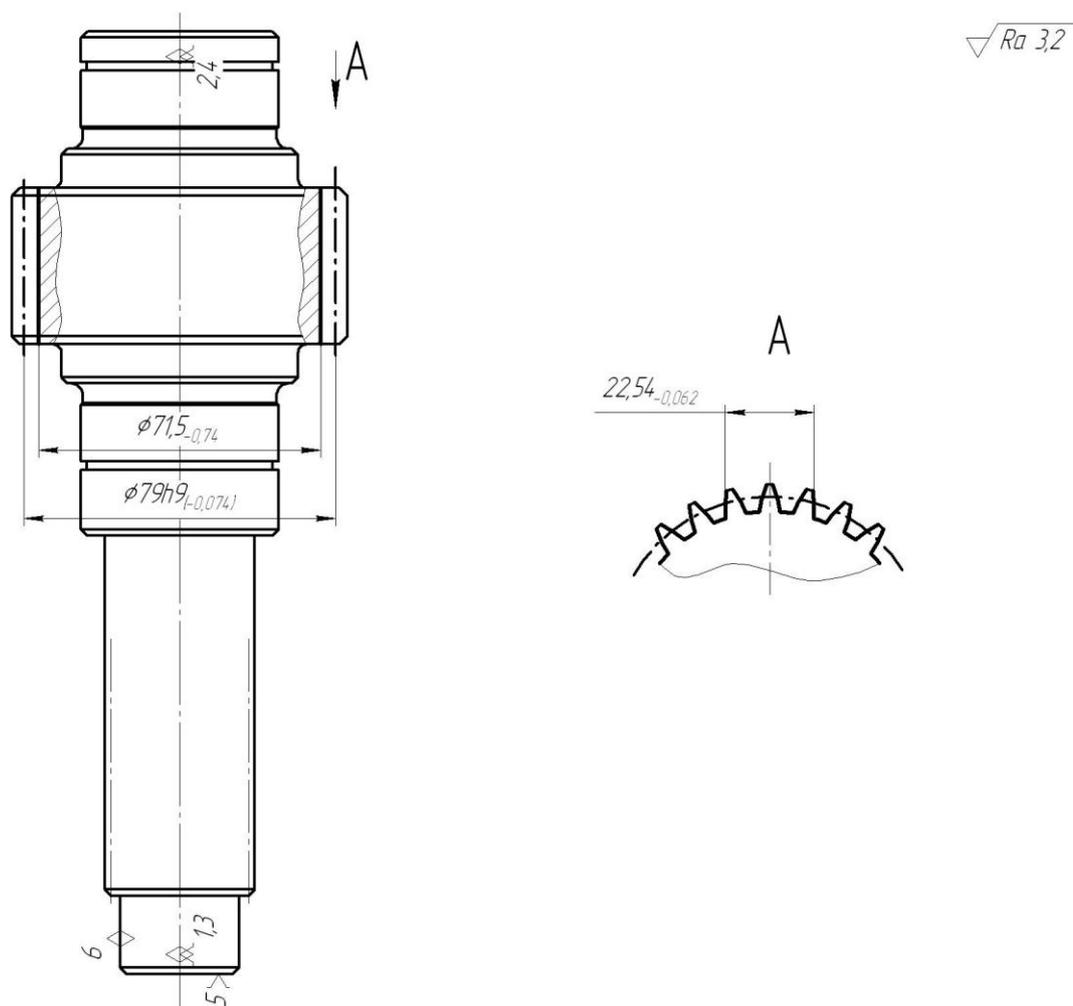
Эскиз операции 035 Зубофрезерная
